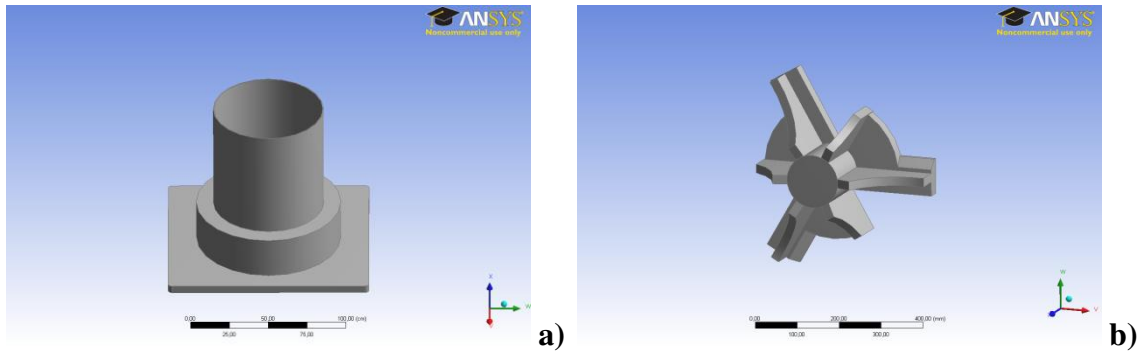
Geometria do equipamento lavador a) Parte estática b) Rotor
